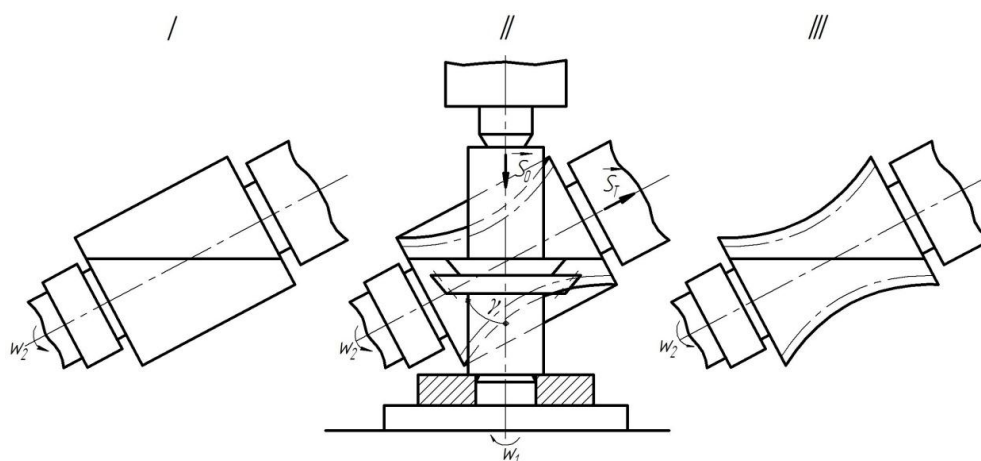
Схема изготовления гиперболического зубчатого колеса
